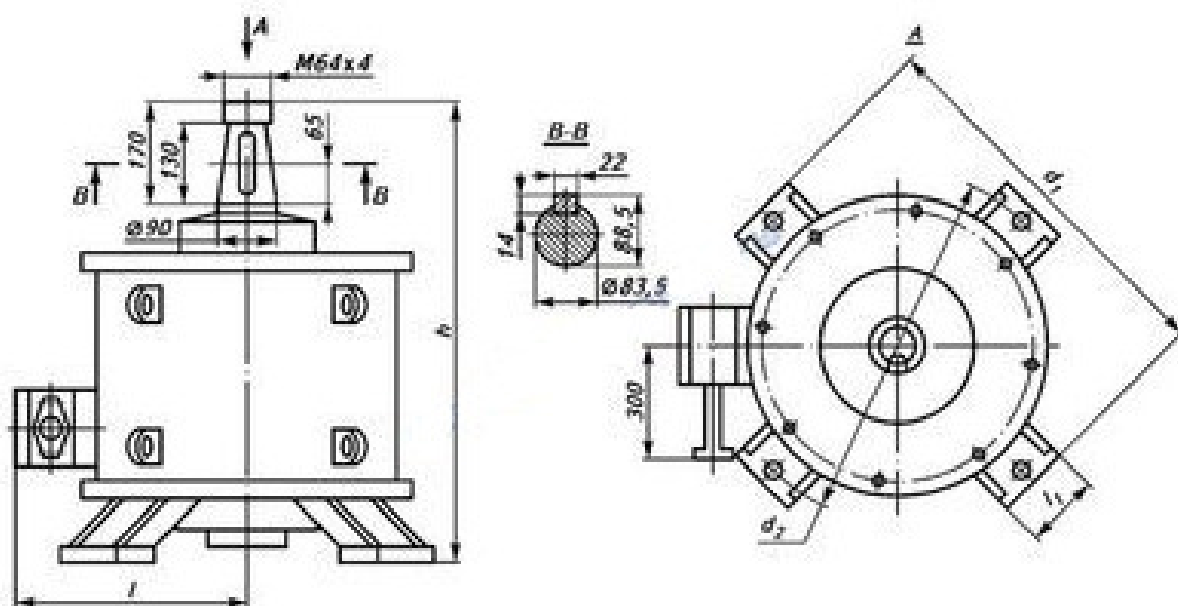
Общий вид двигателей серии ВАСО (с указанием габаритных размеров) [34].
